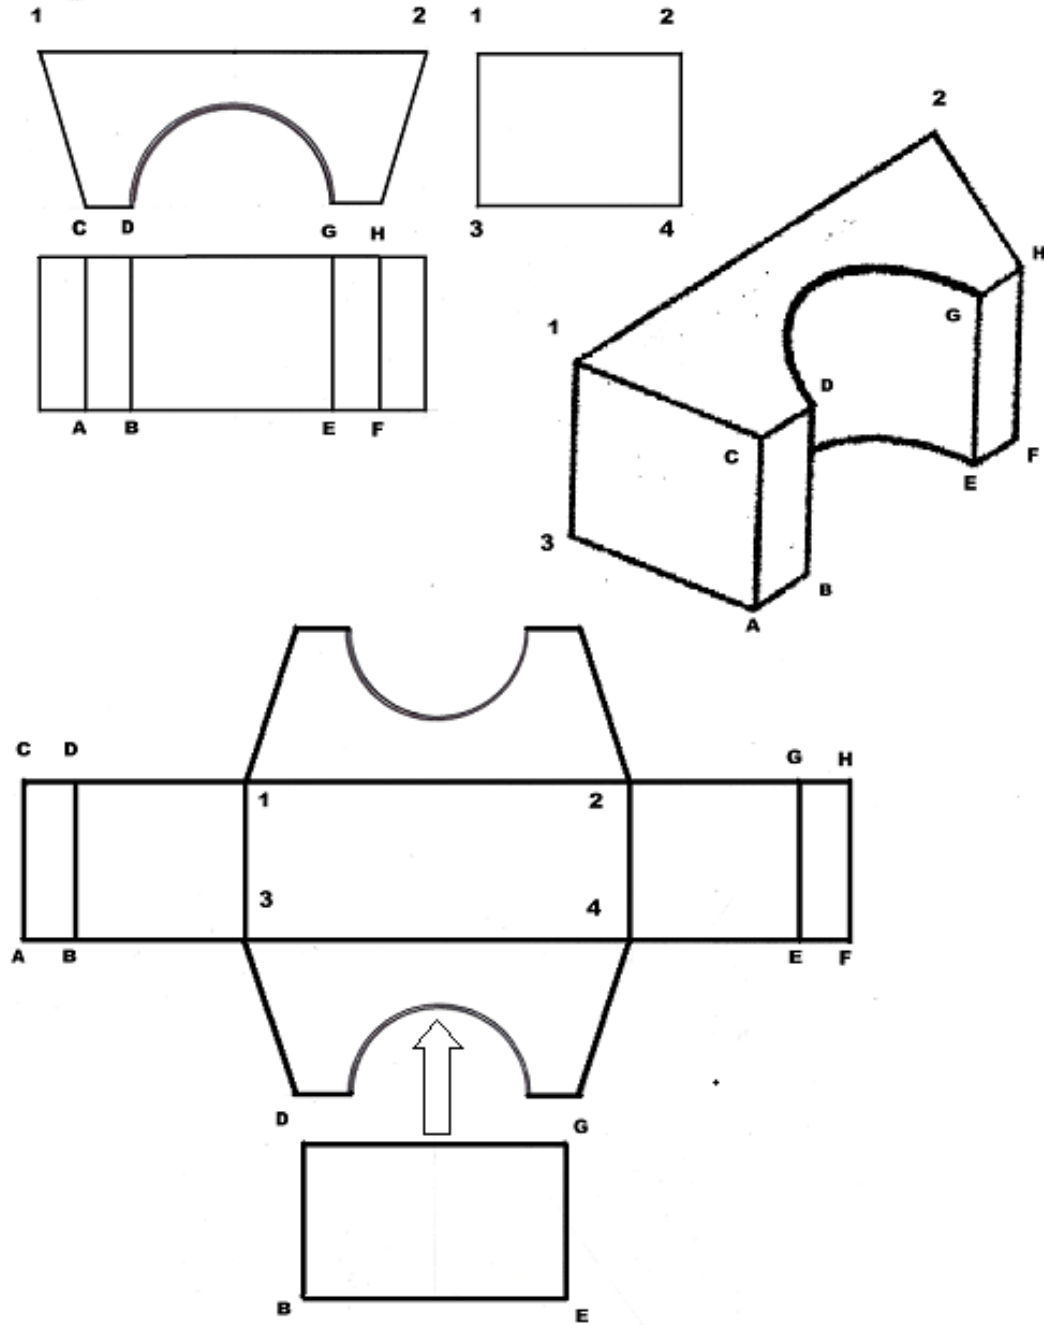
Práctica 25, prisma trapezoidal con corte circular
